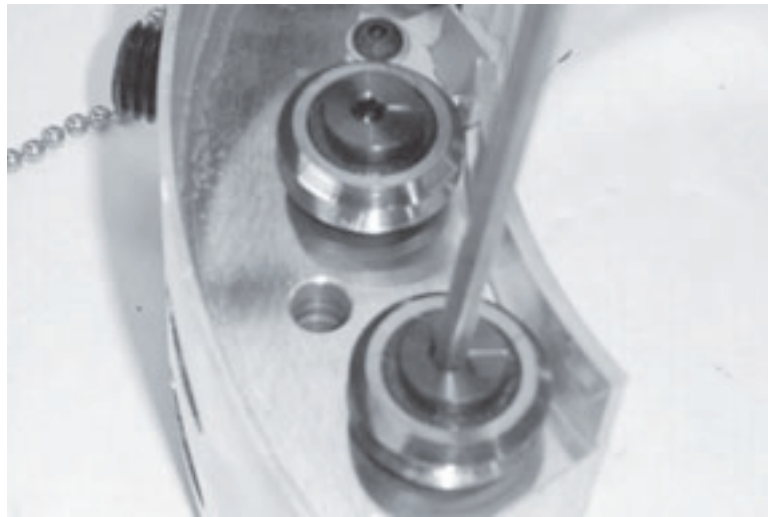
Установите отметки на эксцентриковых валах по направлению к центру вращающейся платформы.
